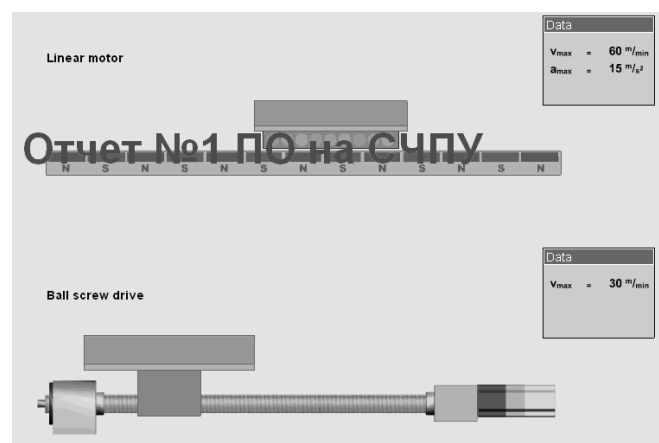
Перемещение суппорта токарного станка с ЧПУ
